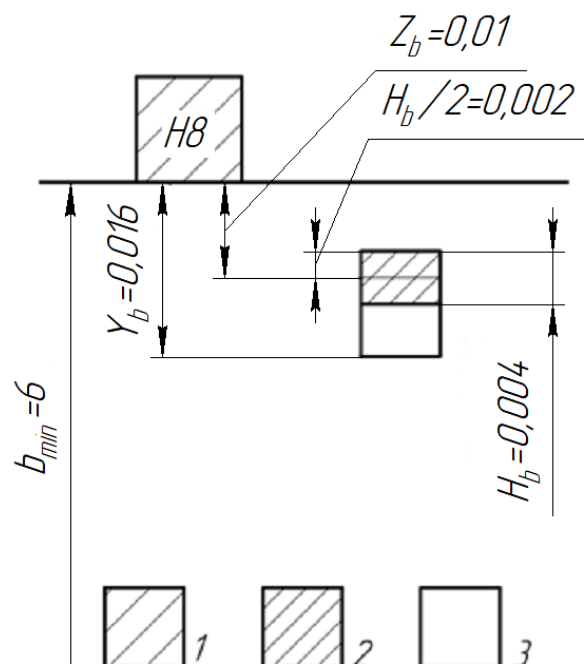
Схема расположения поля допуска размера  $b_k$  калибра-пробки:
